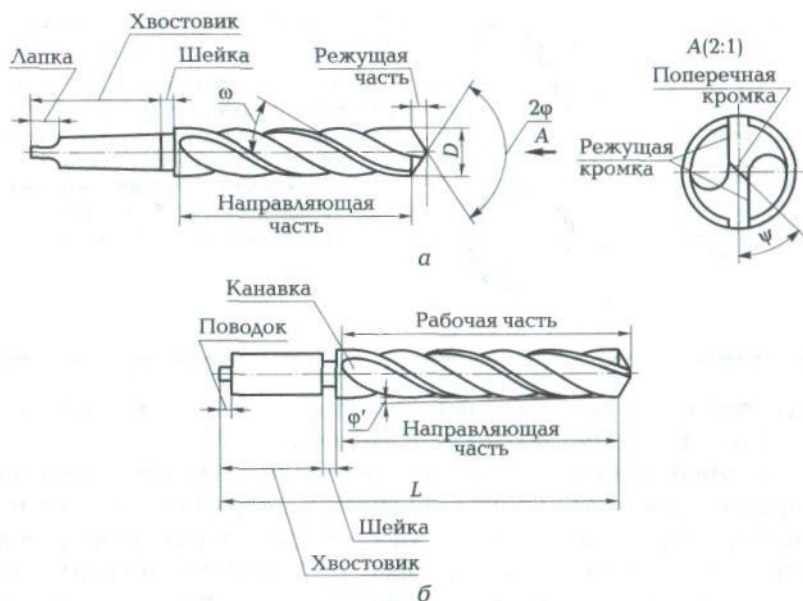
Конструктивные и геометрические параметры спирального сверла
